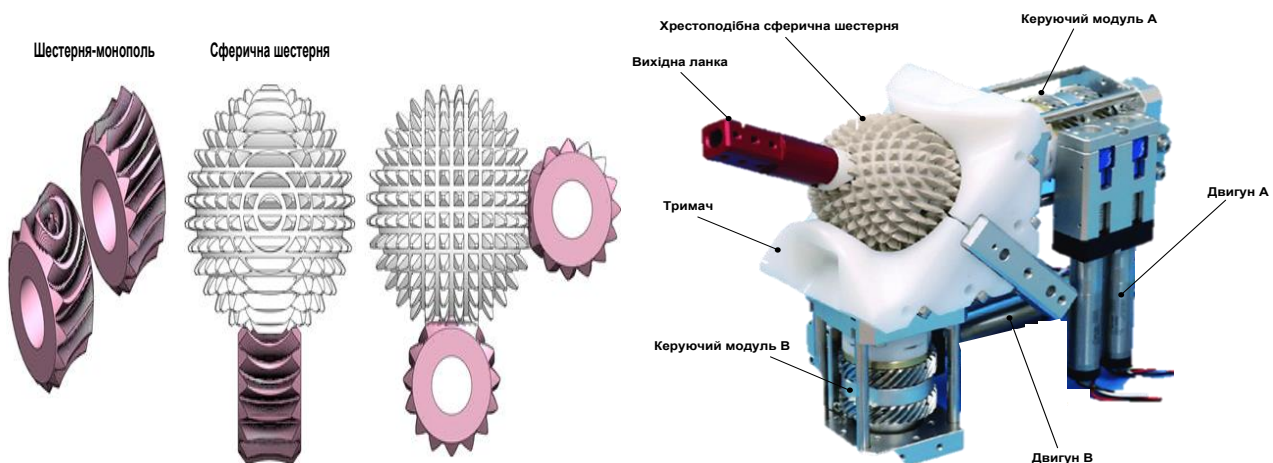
Abenics (активний кульовий шарнірний механізм)
